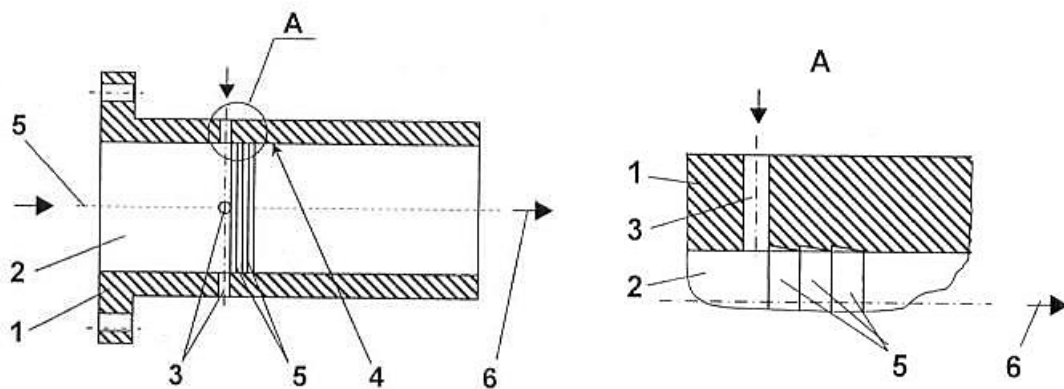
Поздовжній розріз екструзійної головки
